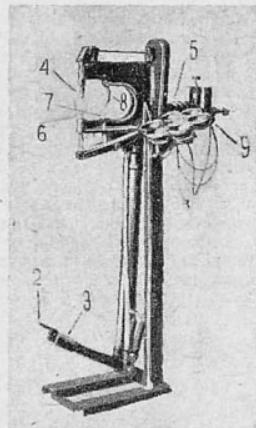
Общий вид станка для сверления и клепки феродо, освоенный трестом Гаро
